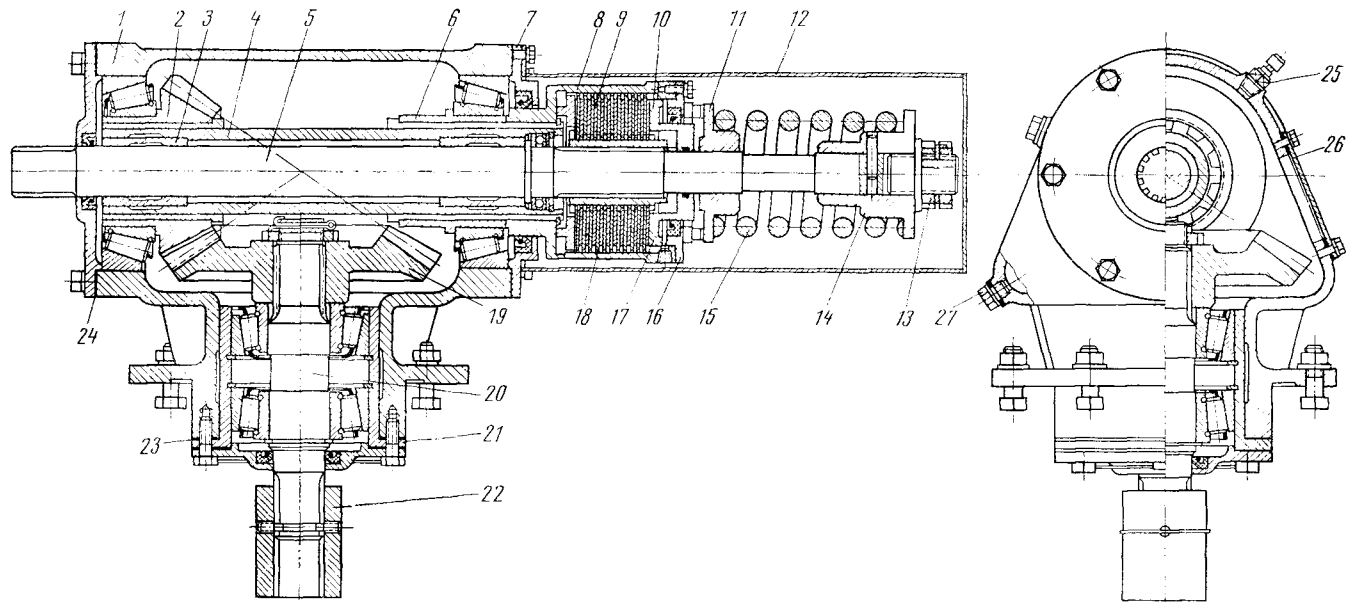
Конический редуктор каналокопателя КФН-1200:
